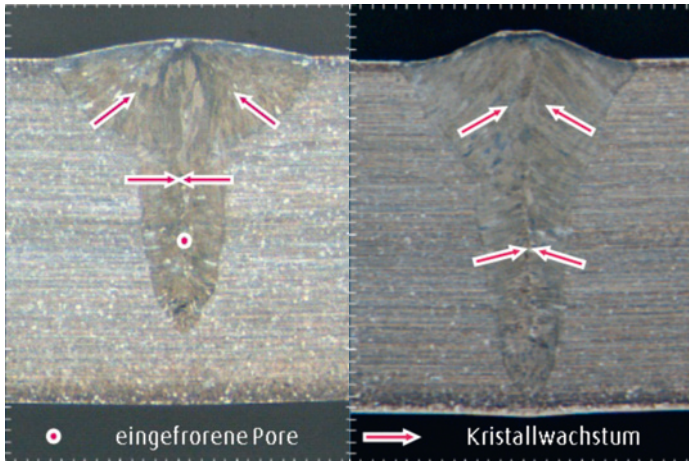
Schliff einer Laserschweißnaht in nichtrostendem Stahl unter inertem Prozessgas
